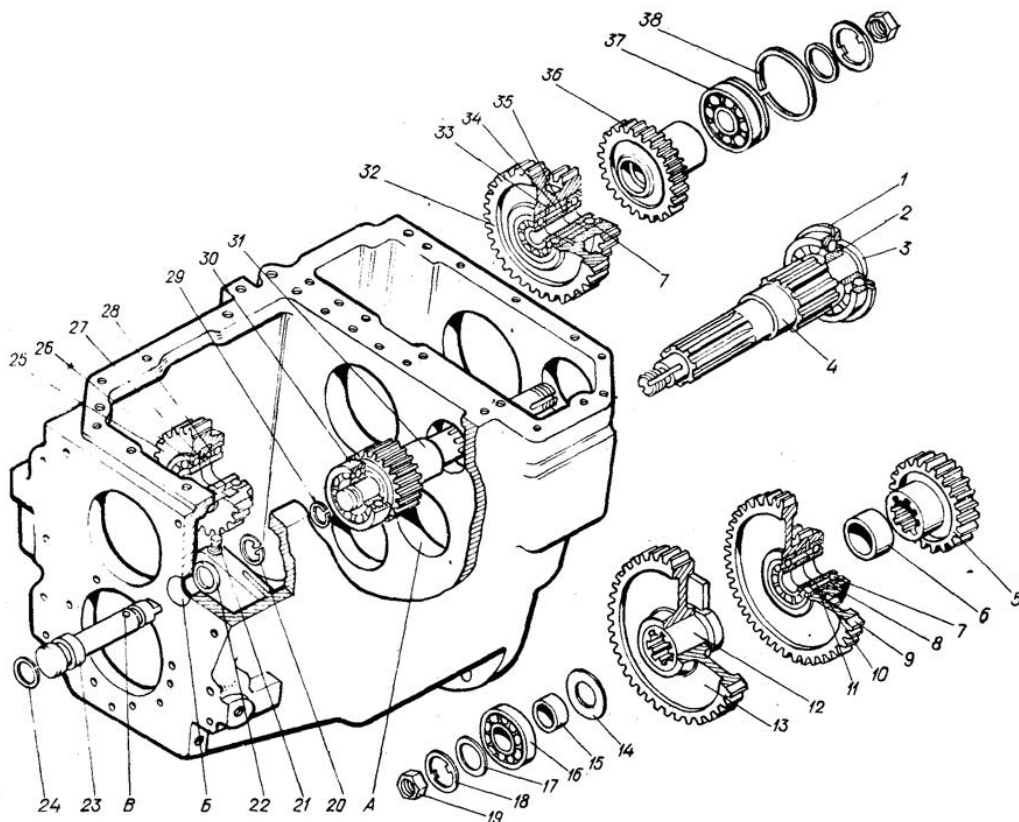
Установка зубчатых колес и валов ходоуменьшителя и заднего хода:
